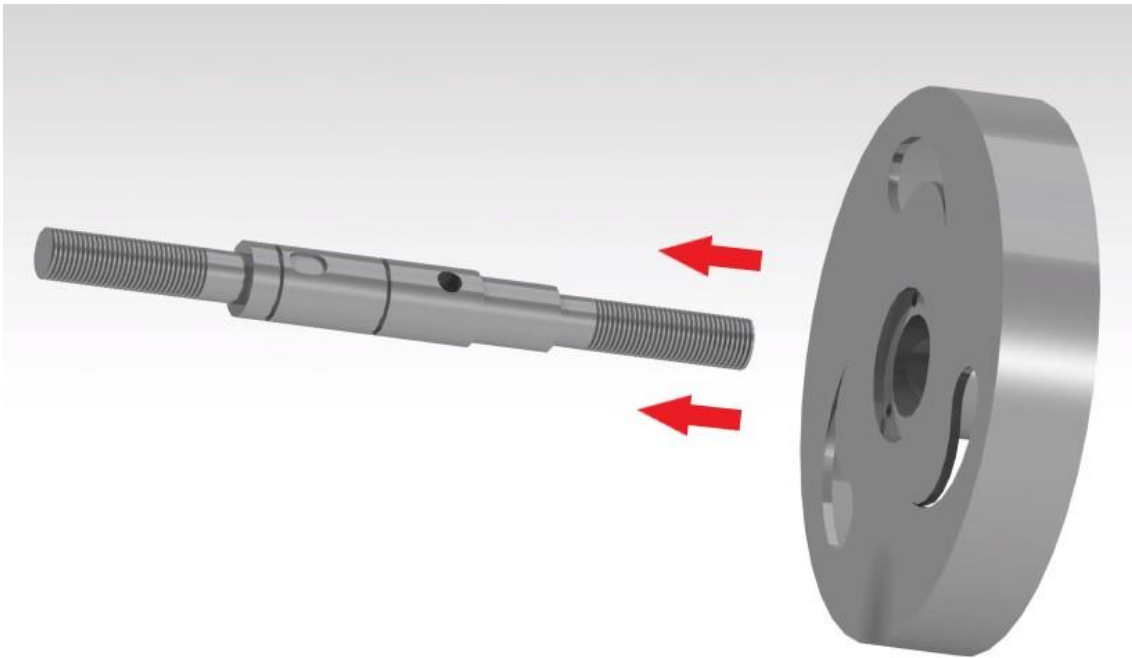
Montaje del conjunto rotor-estator en el eje (Fuente: elaboración propia)
